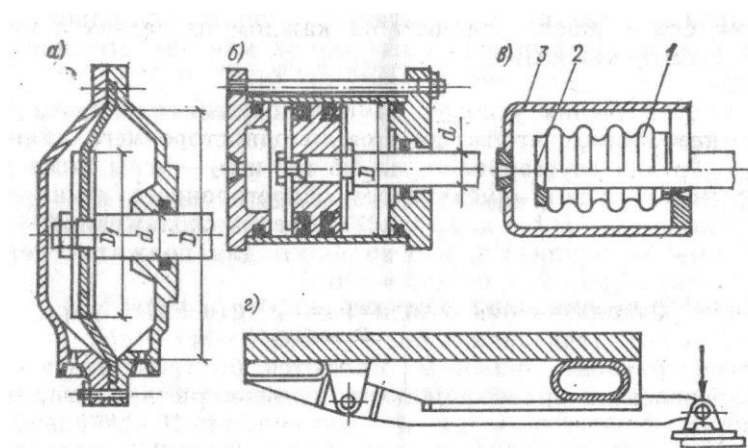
Типы пневмодвигателей: а – пневмокамера; б – пневмоцилиндр двустороннего действия; в – сильфон; г – пневмошланг; D – диаметр тарелки штока; d – диаметр штока; 1 – гофрированная камера; 2 – тарелка штока; 3 – наружная камера
